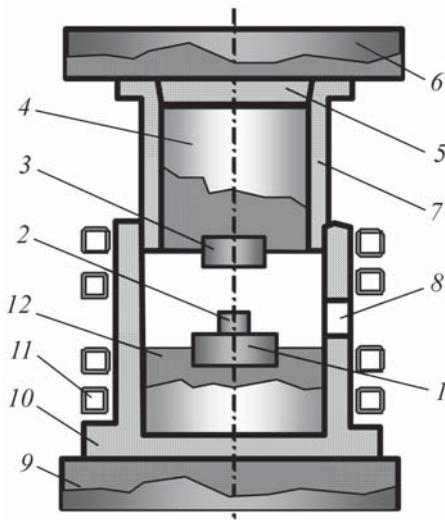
Схема штампового блока для изотермической штамповки:
